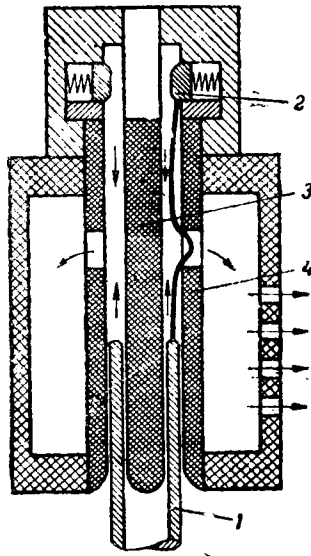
Камера выключателя АЕГ с кольцевой щелью.
